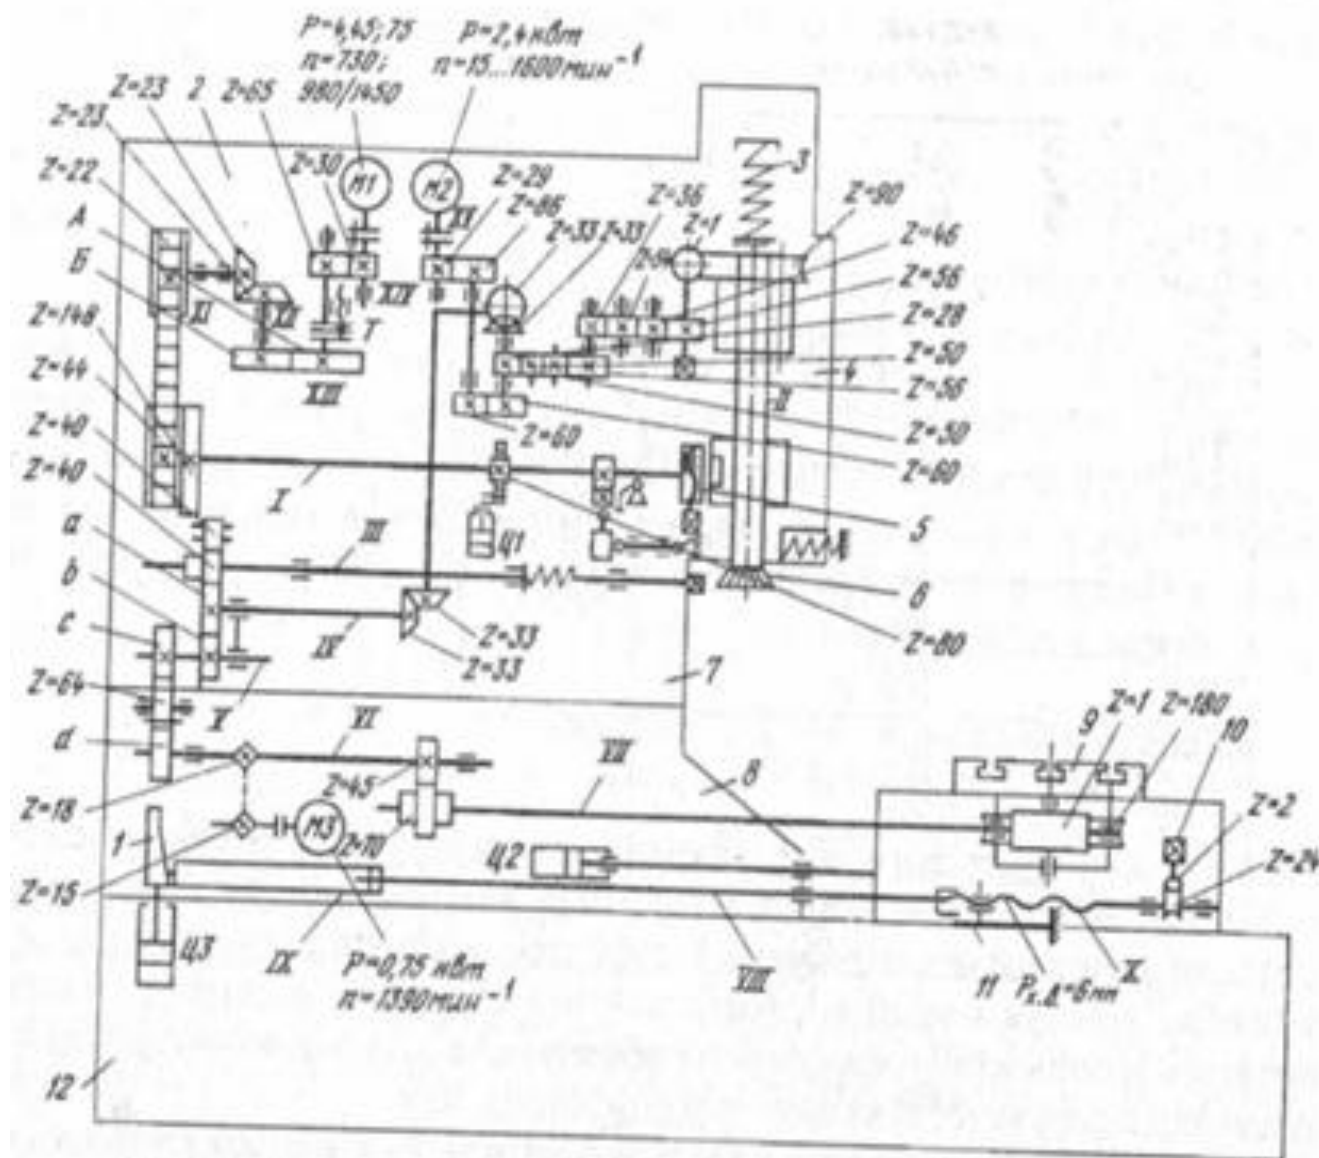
Кинематическая схема зубодолбежного станка модели 5A140.
